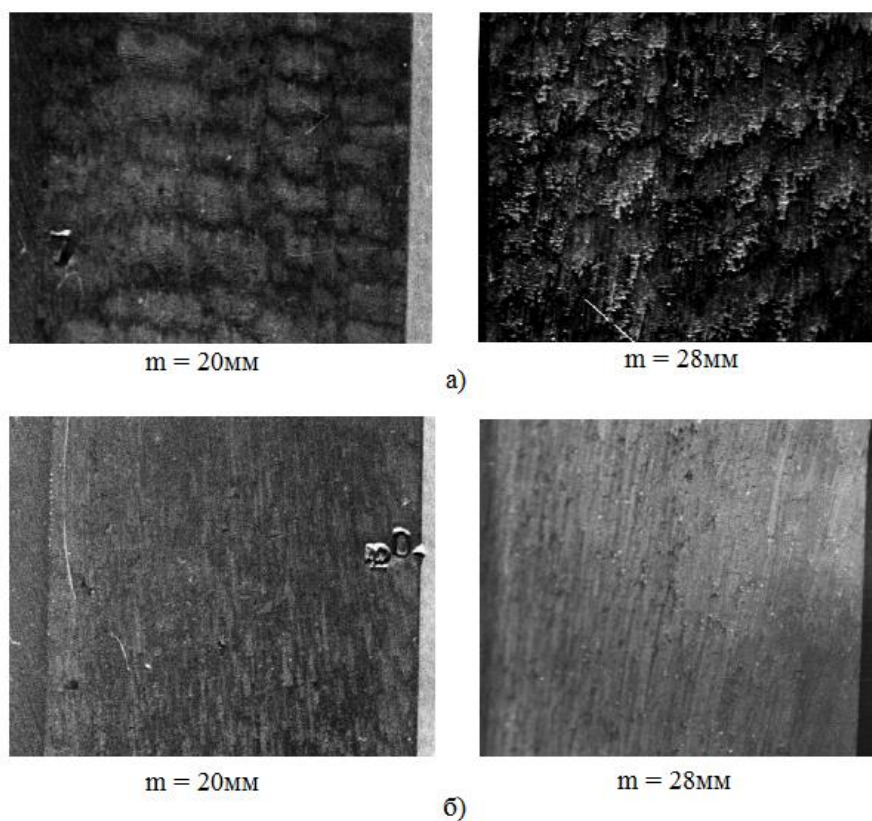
Вид бічної поверхні зубів коліс $m = 20\text{мм}$ и $m = 28\text{мм}$ ($\Delta = 0,5\text{м}$; $S = 4\text{ мм/об}$; $V = 16\text{ м/хв}$): а - оброблення стандартною фрезою; б - оброблення фрезою з роздільною схемою формоутворення
